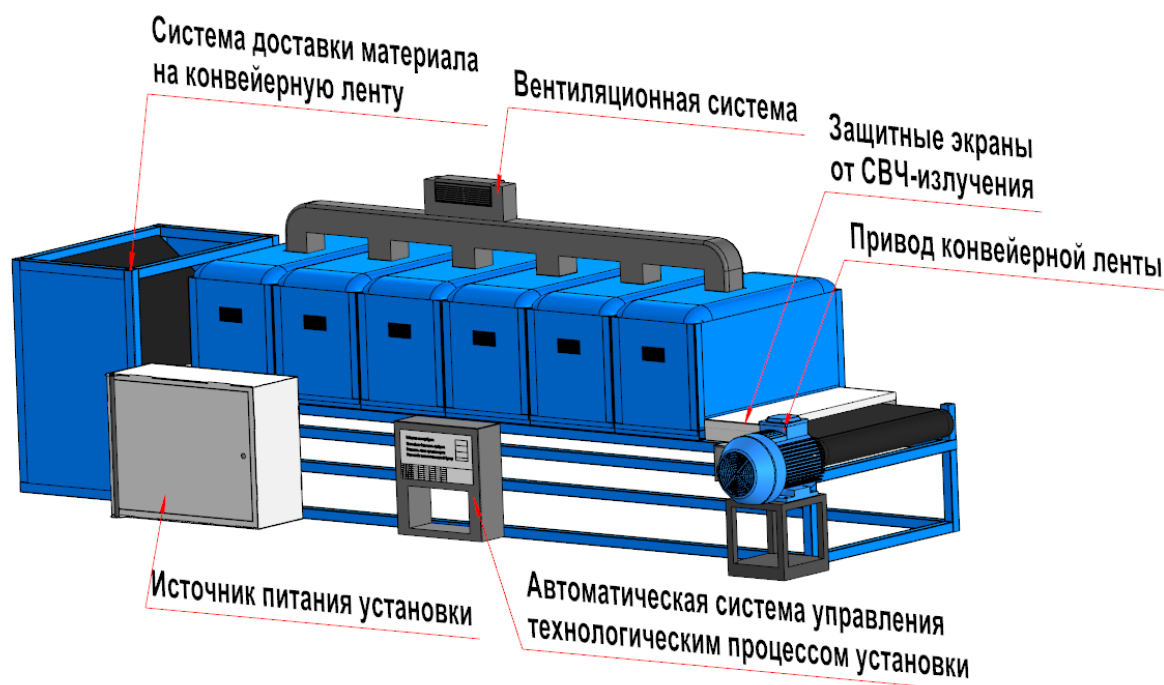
Конструкция СВЧ-установки конвейерного типа
